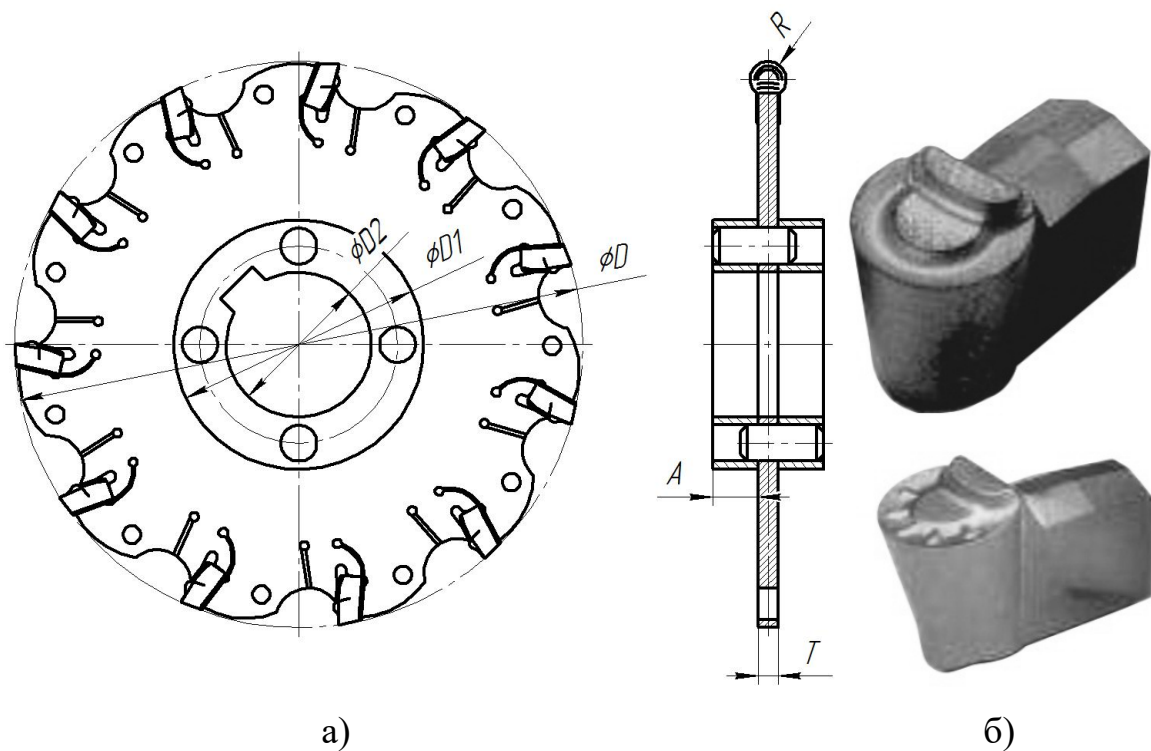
Конструкція фрези чистової по дну міжзубової западини
